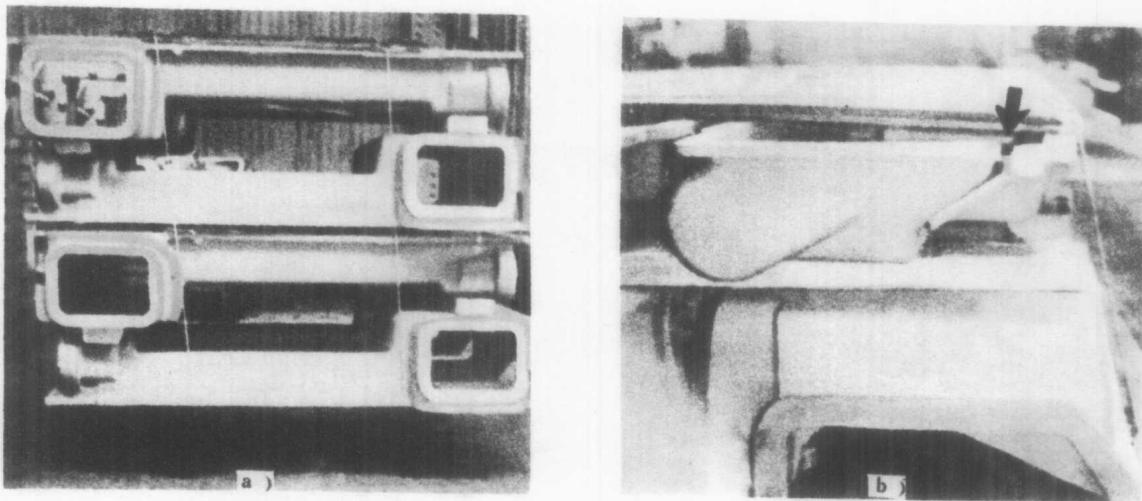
a) 铸件在垫板上捆扎过紧 b) 造成的铸件断裂
